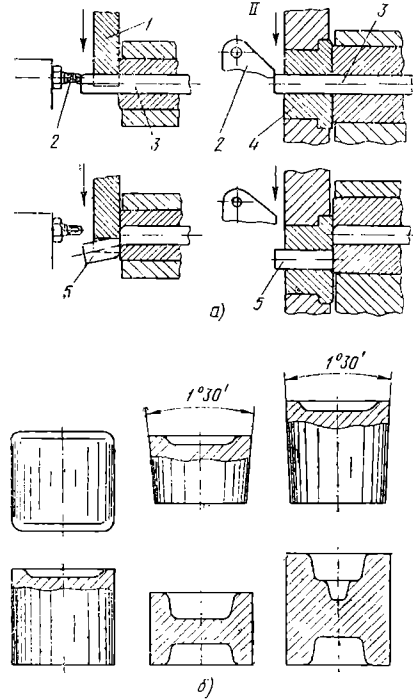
Изготовление заготовок для холодной объемной штамповки:
